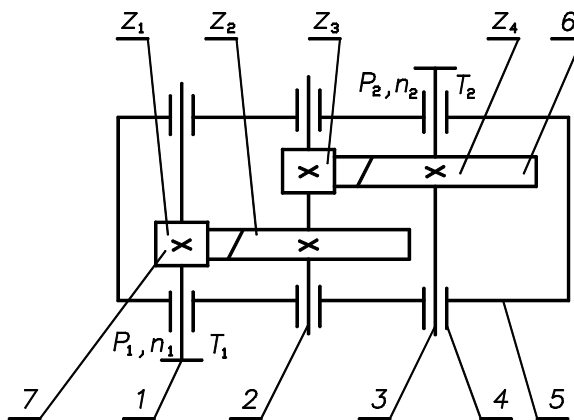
Кинематическая схема редуктора с косозубым зацеплением:
